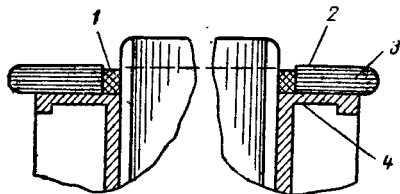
Цилиндрический обмоткодержатель, прилегающий к активной стали якоря или ротора:
